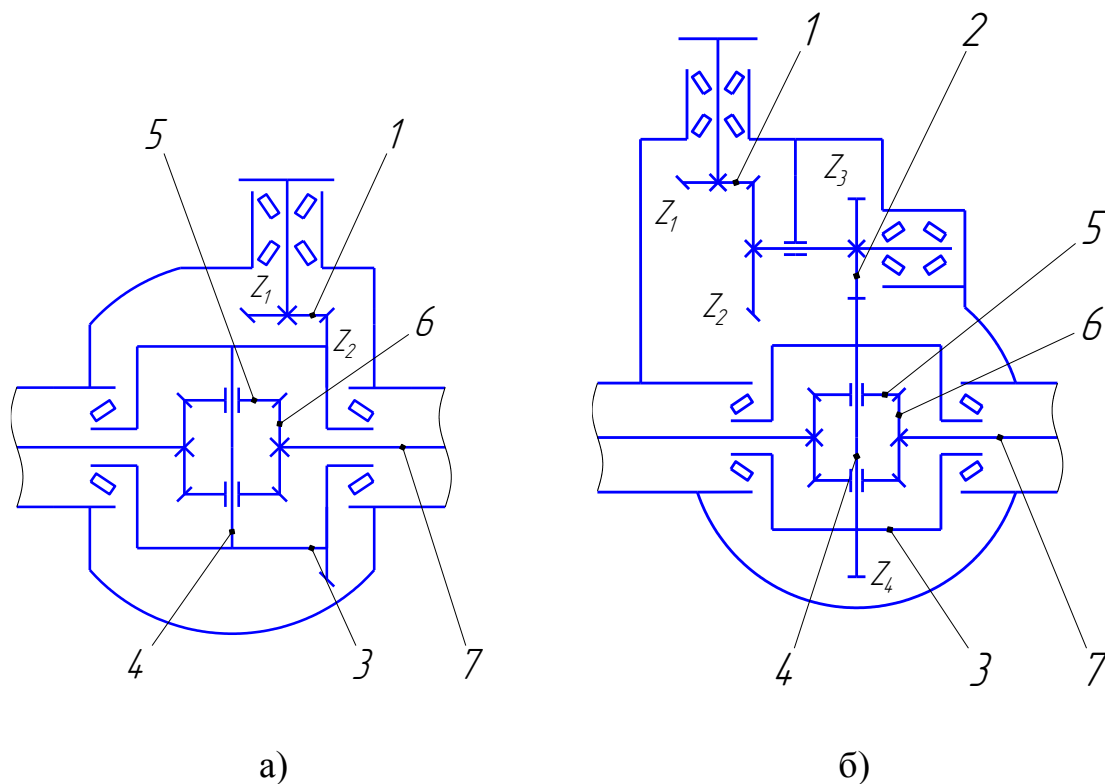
Кинематическая схема главной передачи и дифференциала: а – одинарная; б – двойная; 1 – коническая ступень, 2 – цилиндрическая ступень, 3 – корпус дифференциала, 4 – ось сателлитов, 5 – сателлиты, 6 – шестерня полуоси, 7 – полуось
